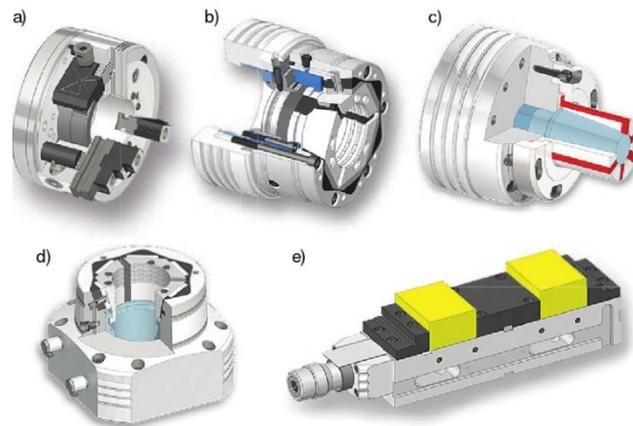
Werkstückspannmittel: a) Backenfutter, b) Spannzangenfutter, c) Spanndorn, d) Spannstock, e) Maschinenschraubstock; Quelle: Taschenbuch der Werkzeugmaschinen, Hanser
